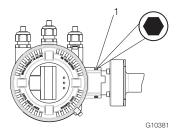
Вращение корпуса измерительного преобразователя 1 Крепежный винт | 2 Корпус измерительного преобразователя
